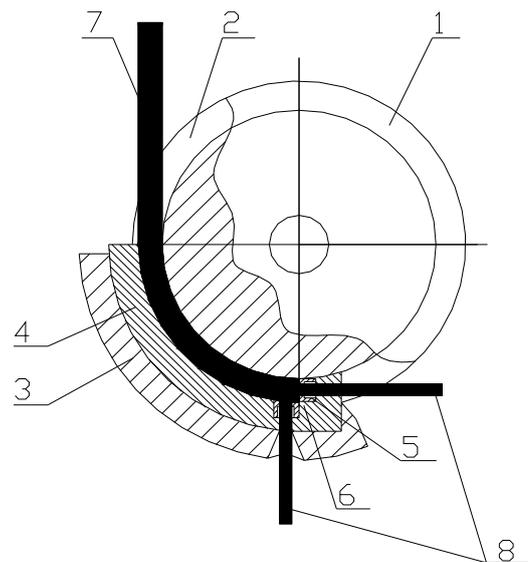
Принципиальная схема реализации процесса непрерывного прессования по способу Конформ: 1 – рабочее колесо; 2 – кольцевая канавка; 3 – башмак; 4 – кольцевая вставка; 5 – вставка; 6 – матрица; 7 – заготовка; 8 – изделие
